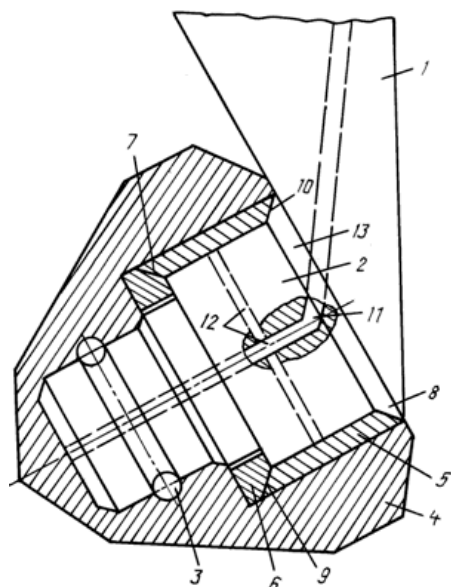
Конструкція опори з плаваючою втулкою та конічними поверхнями тертя
